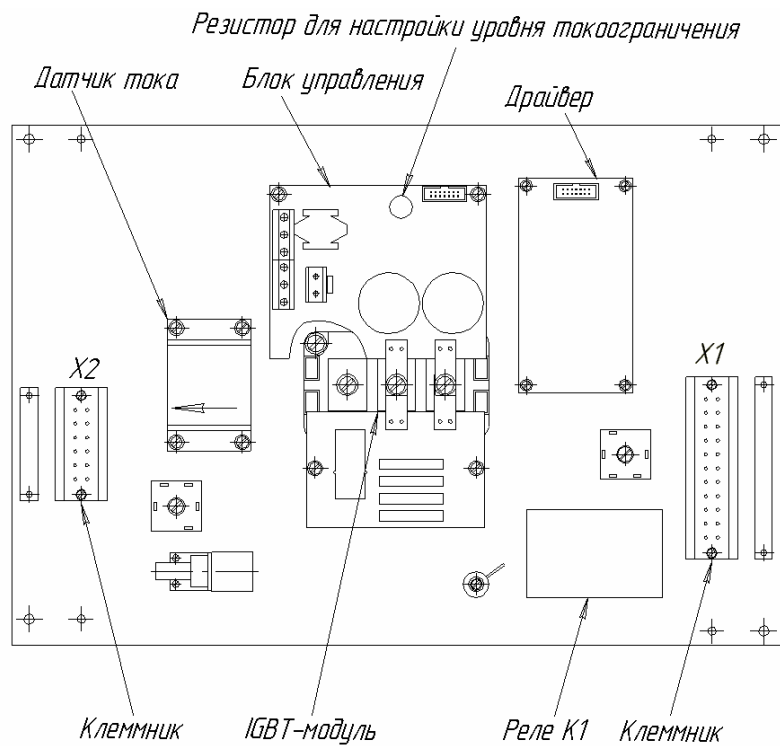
Внешний вид устройства и расположение элементов.
